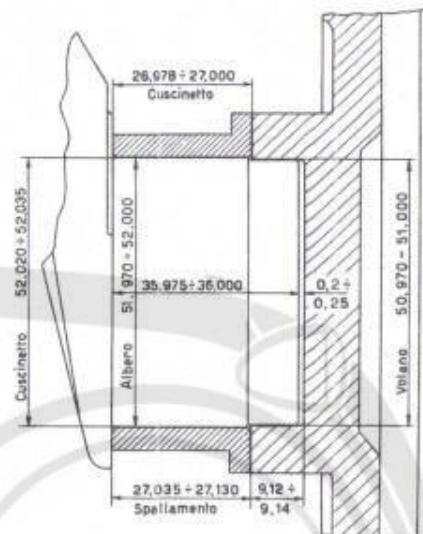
Particolare del supporto posteriore del motore 500 B con le tolleranze di montaggio del cuscinetto e del volano motore sull'albero manovella.
